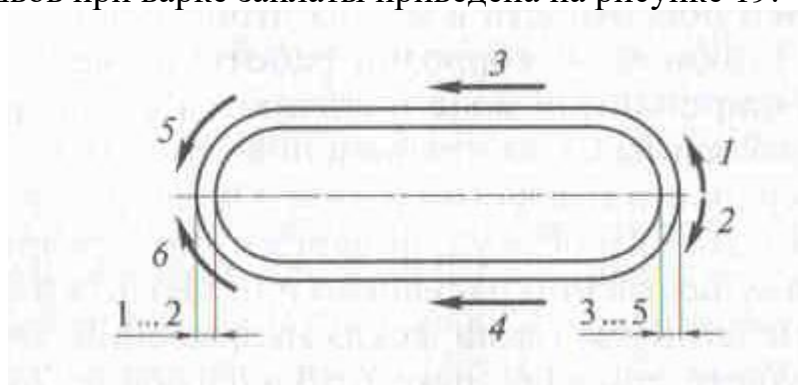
Последовательность выполнения сварного соединения при варке заплата
